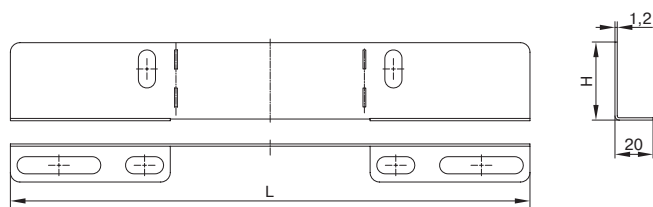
Редукция для лотков лестничных H55 / Figure D.1 — Cable ladder reducer H55
